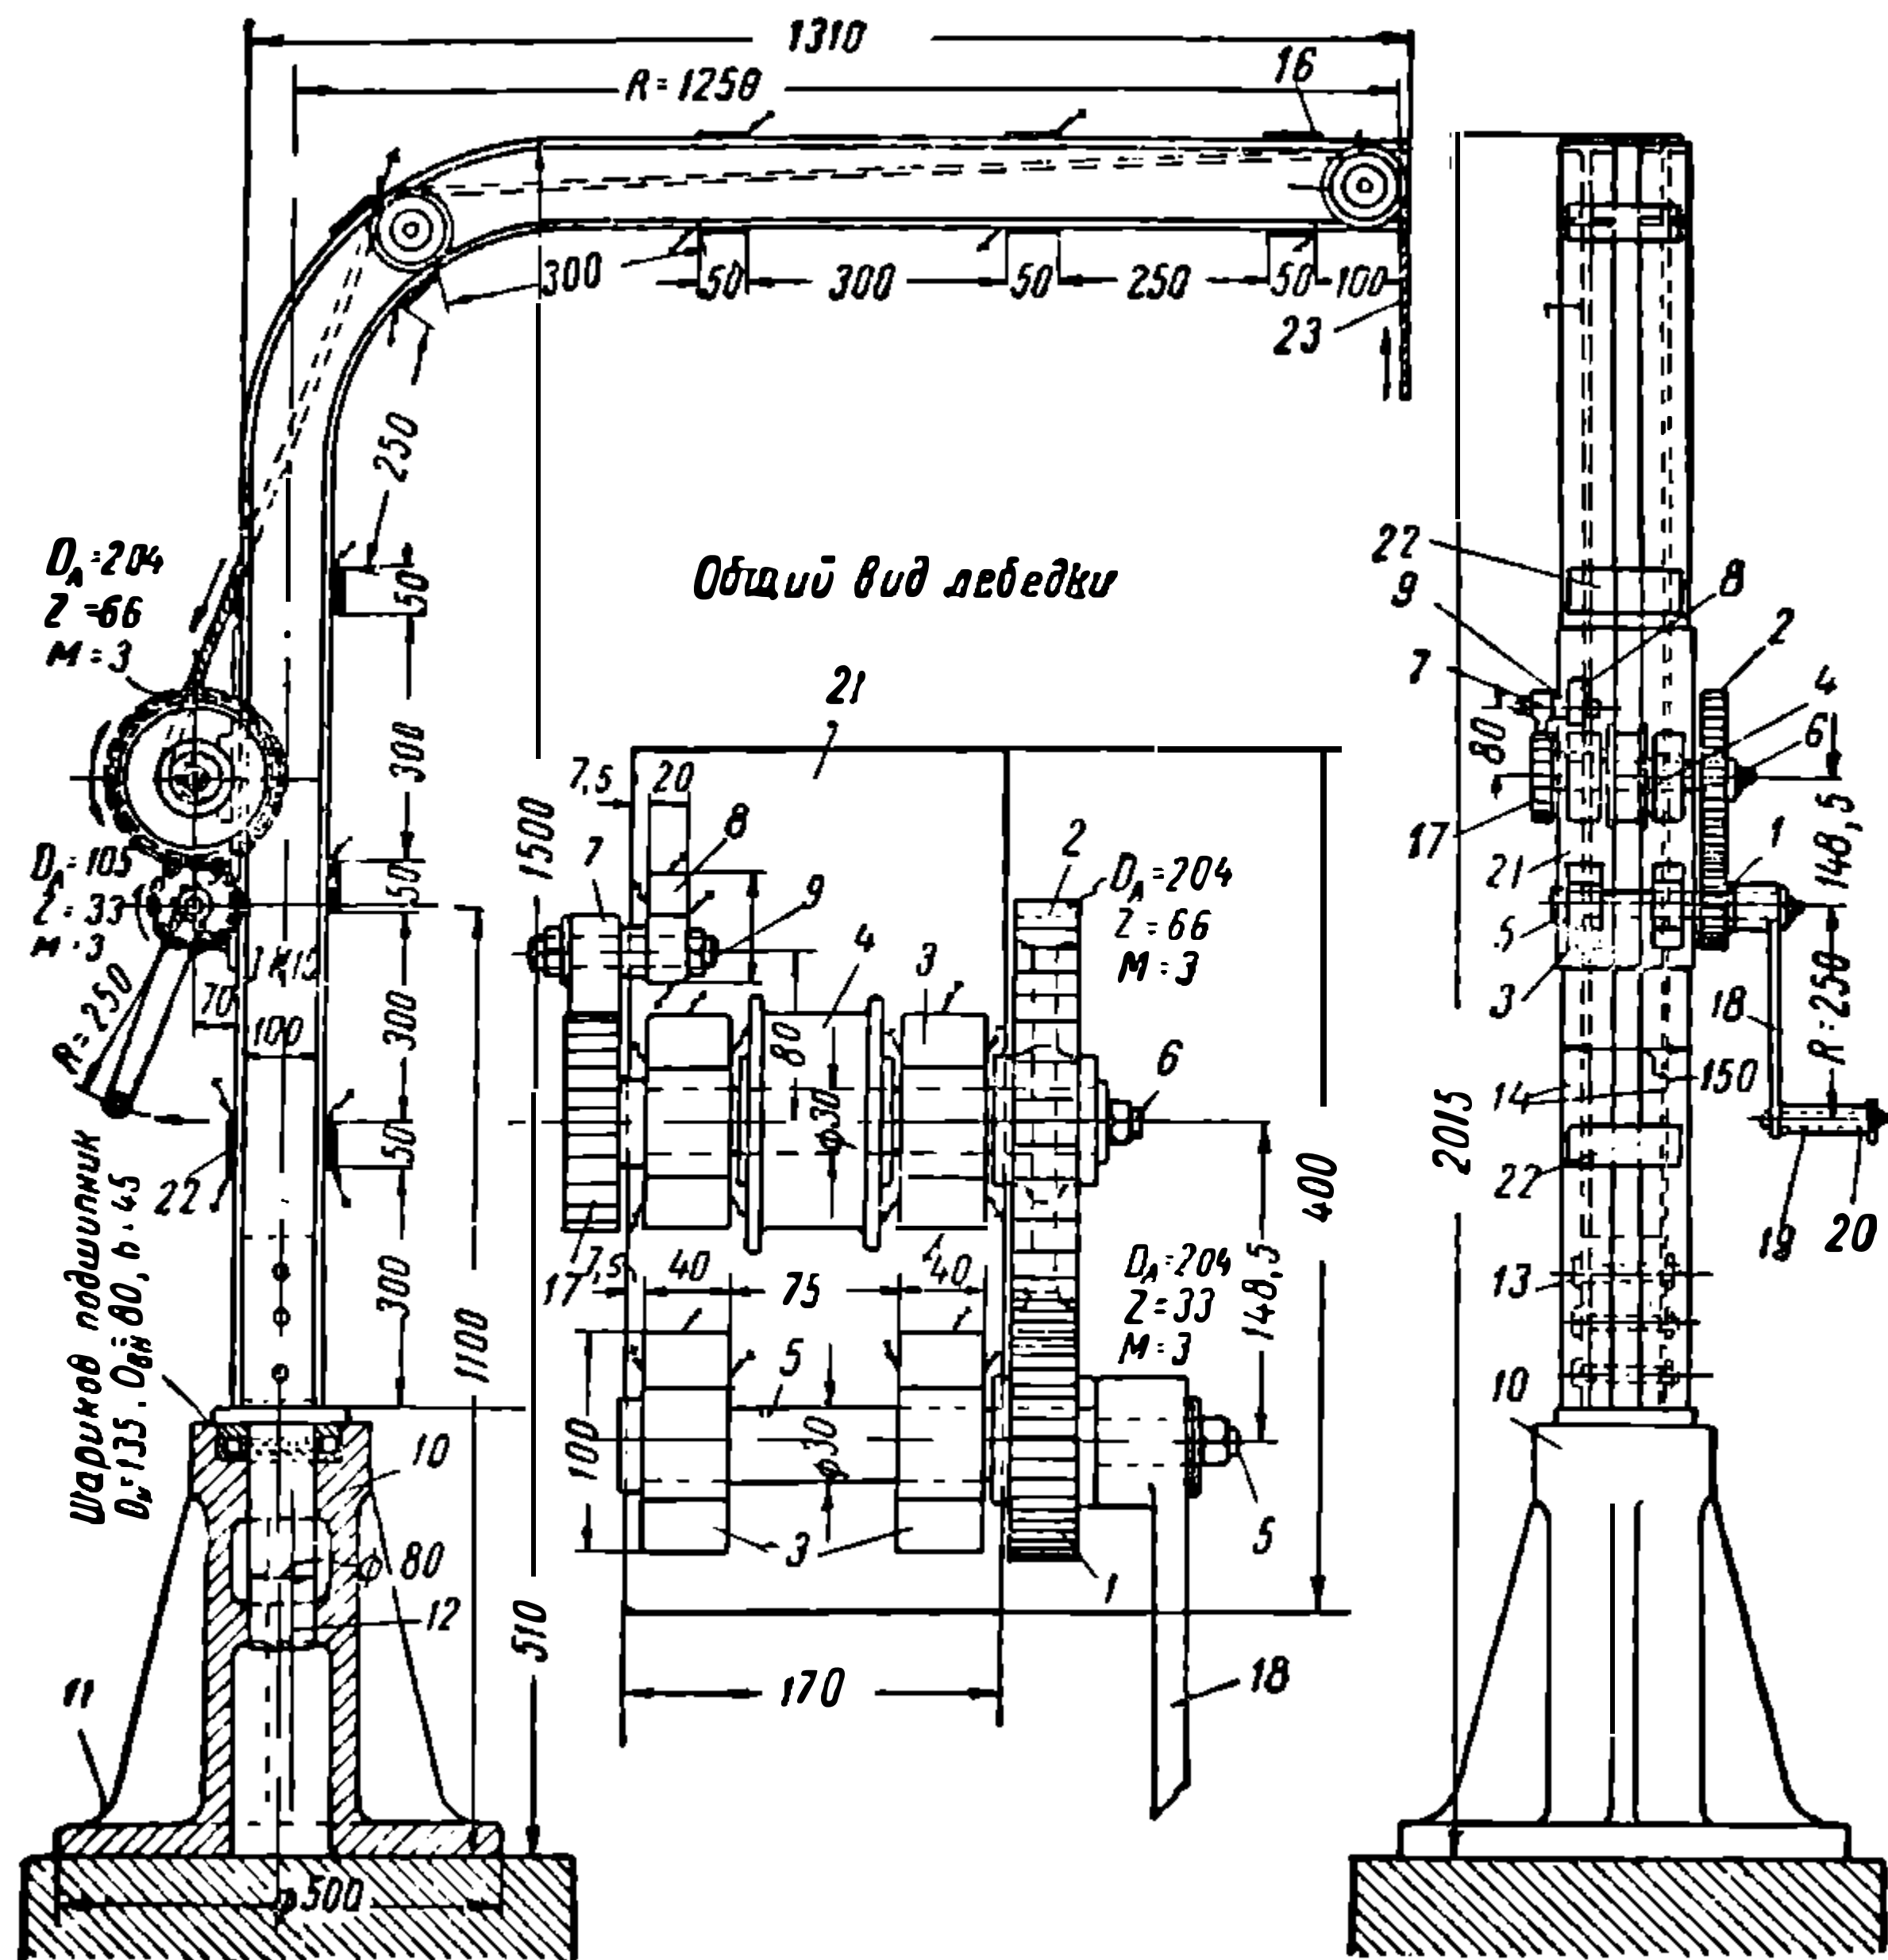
Устройство поворотного стола с тележкой для тигля, служащего для заливки подшипников
